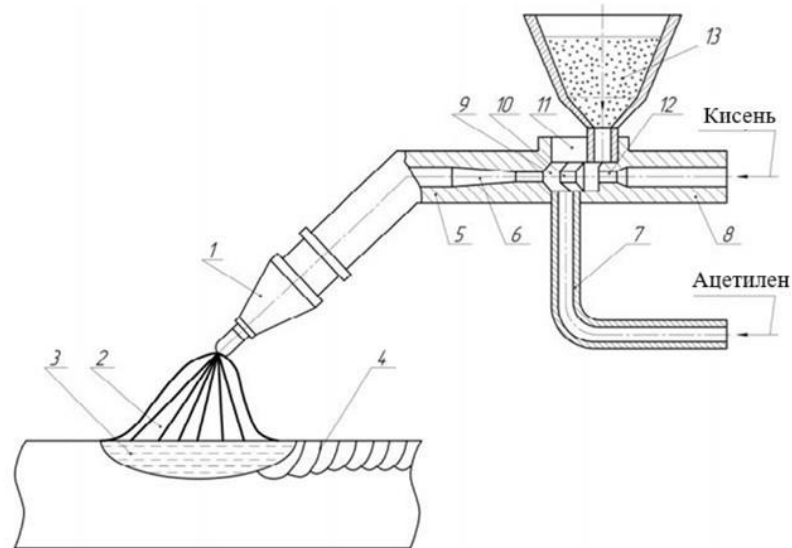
Схема газопорошкового наплення порошку: 1 – мундштук; 2 – полум'я; 3 – зварювальна ванна; 4 – наплавлений шар; 5 – трубка; 6 – канал; 7 – ацетиленова трубка; 8 – киснева трубка; 9 – камера змішування; 10, 12 – ейектори; 11 – змішувальна камера; 13 – порошок [2].
